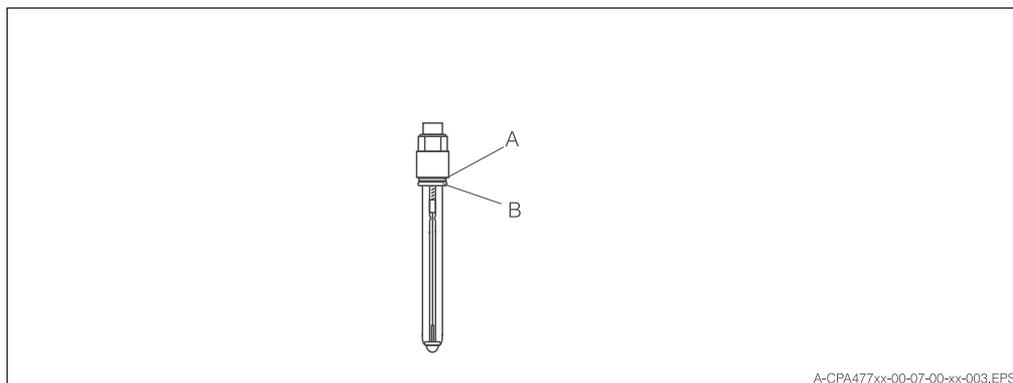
Anello di spinta A e O-ring B di un elettrodo a gel
